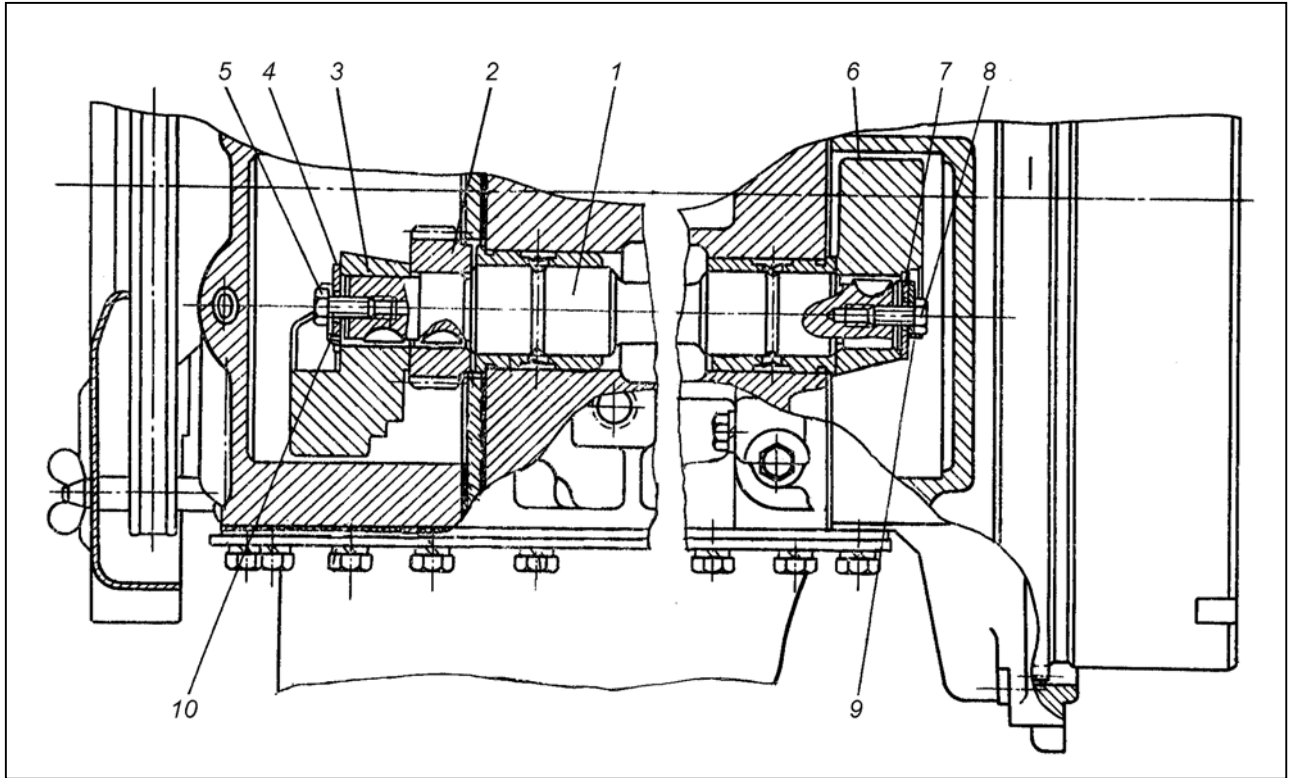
К сборке и установке механизма уравнивания двигателей Д21А, 120, 130, 130Т и модиф.: 1 – валик механизма; 2 – ведомое зубчатое колесо; 3 – передний груз; 4, 7 – упорные шайбы; 5, 8 – болты; 6 – задний груз; 9, 10 – шайбы стопорные.
